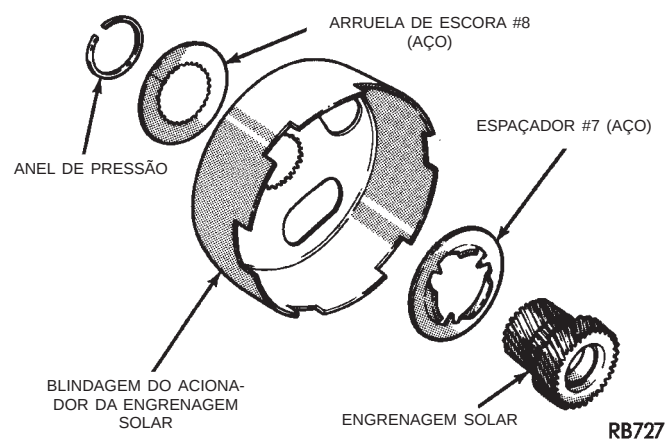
Componentes da Blindagem do Acionador da Engrenagem Solar
